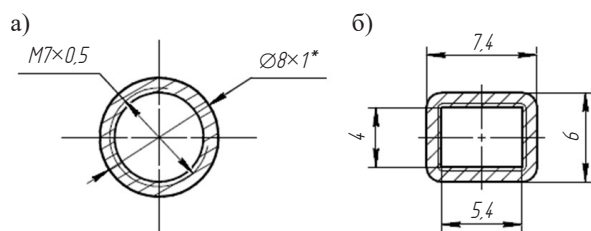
Поперечний переріз гравітаційної ТТ в зоні нагріву: а — початкова форма; б — форма після пресування
